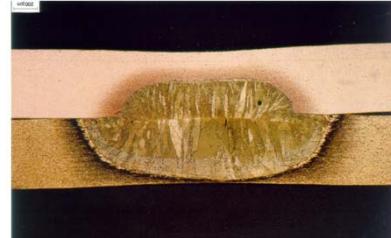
Kupfer-Messing-Punktschweißung Vergr. = 40 (45)
